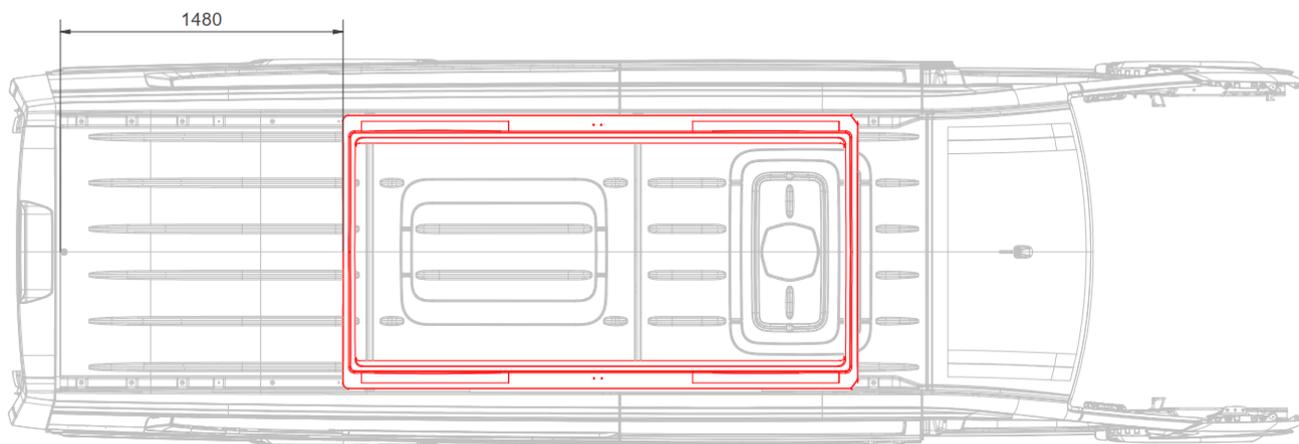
VW Crafter L5H3 (L = 7391 mm) [G0002143-001]
